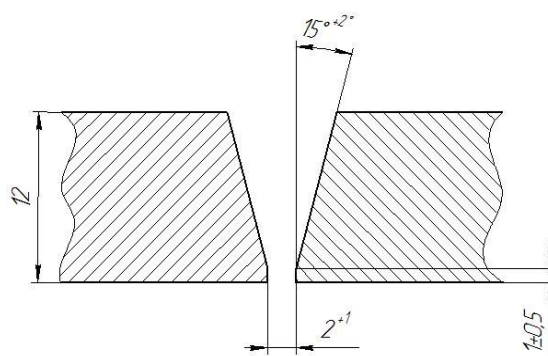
Подготовка под сварку труб диаметром 325 мм толщиной стенки 12 мм
